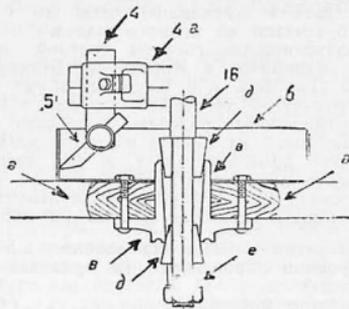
Разрез автомобильного колеса с тормозным барабаном и резцом, установленным для расточки барабана
